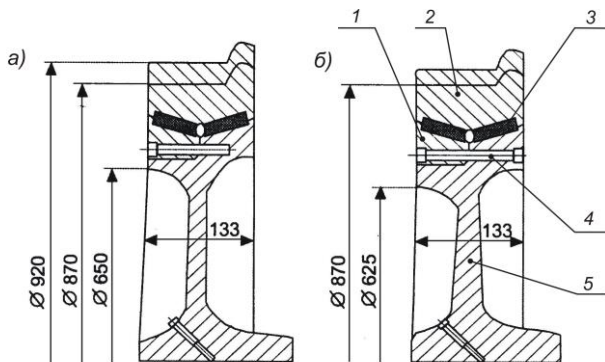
Колеса типа ВА65 с колесным центром, выполненным из алюминиевого сплава (а) и из стали (б)
